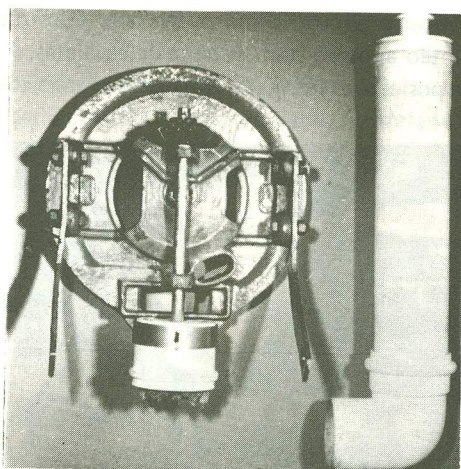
Detalhe da montagem do dispositivo à base da plantadeira visto por baixo.
